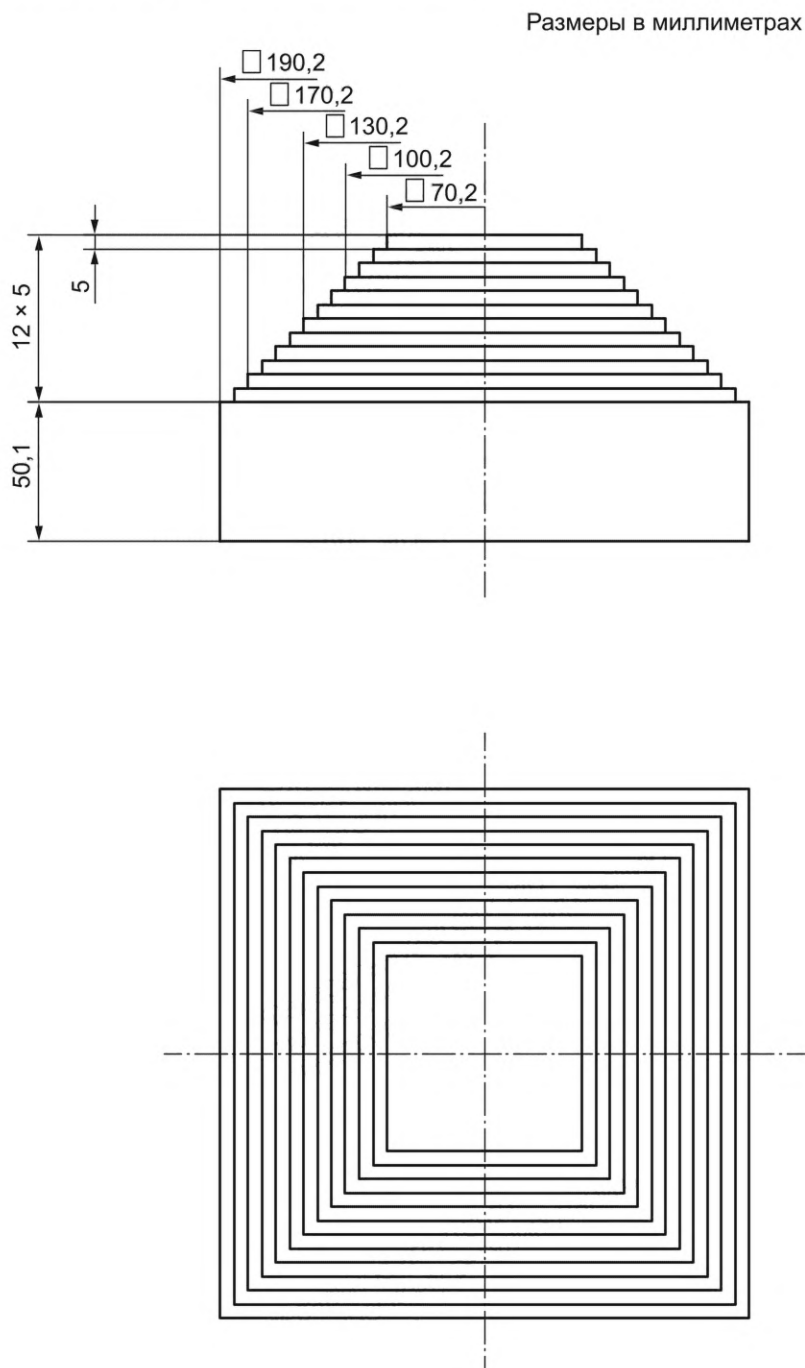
Форма и размеры заготовки детали с припуском на чистовую обработку
